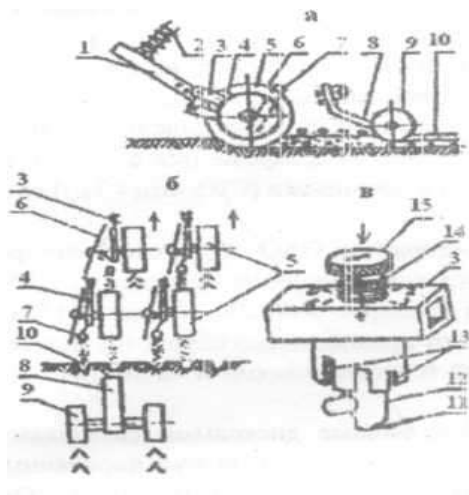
Однодисковая сошниковая группа к сеялке СЗ-5,4: а, б – схема работы сошников; в – регулятор глубины: 1 – поводок; 2 – пружина; 3 – корпус сошника; 4 – регулятор; 5 – опорно-прикатывающий каточек; 6 – диск; 7 – направитель семян; 8 – пружинный поводок; 9 – прикатывающий каточек; 10 – семена; 11 – хвостовик; 12 – штифт; 13 – прорезь; 14 – пружина; 15 – головка-указатель
